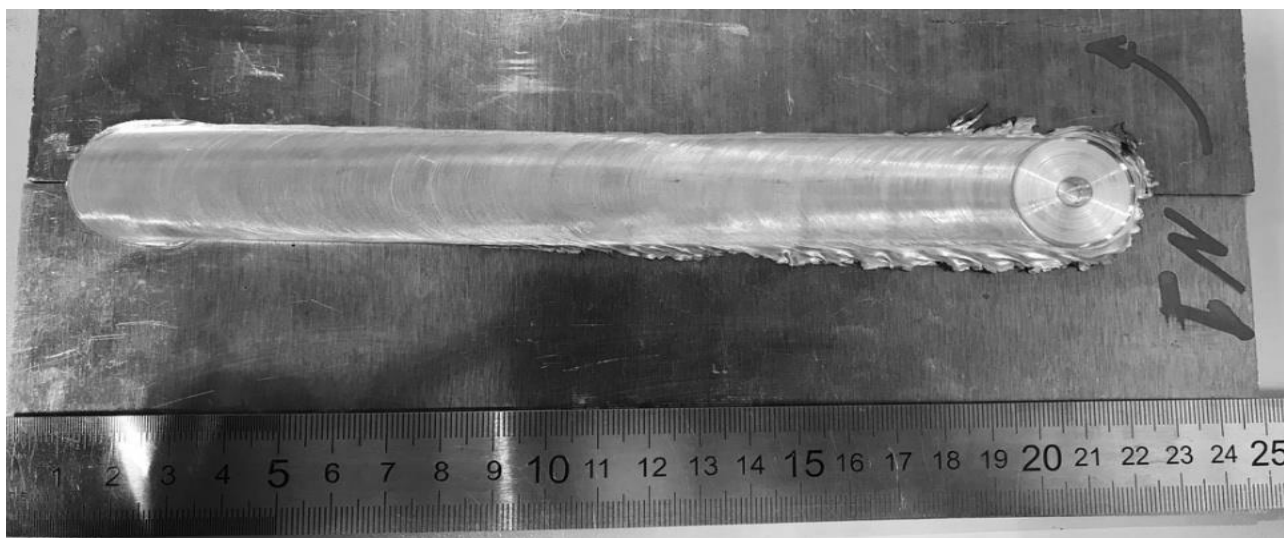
Сварка алюминиевого листа толщиной 6,0 мм способом СТП
